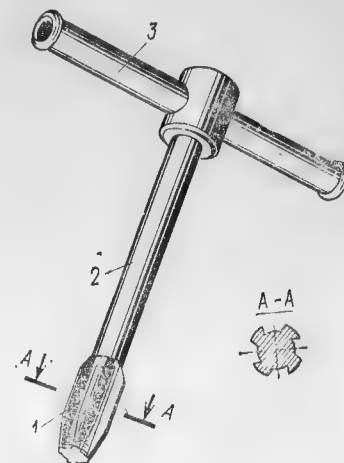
1 — головка; 2 — корпус; 3 — вороток
